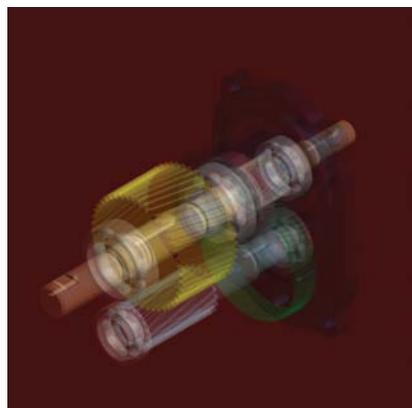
, Рис. 6, Рис. 7. Кадры видео-ролика сборки-разборки детали «Редуктор»
